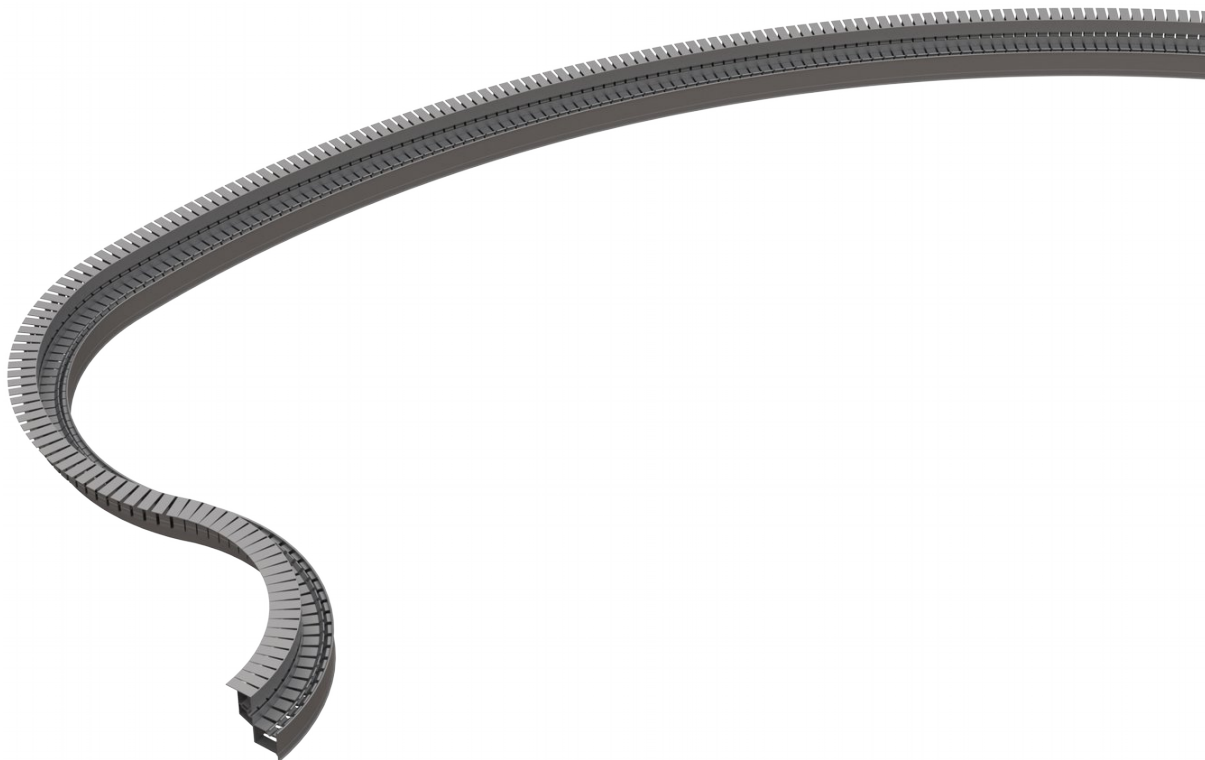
Сборка из криволинейных сегментов. Показанный образец собран из профилей КП и НП (см. рис. 2.4, стр. 7).
